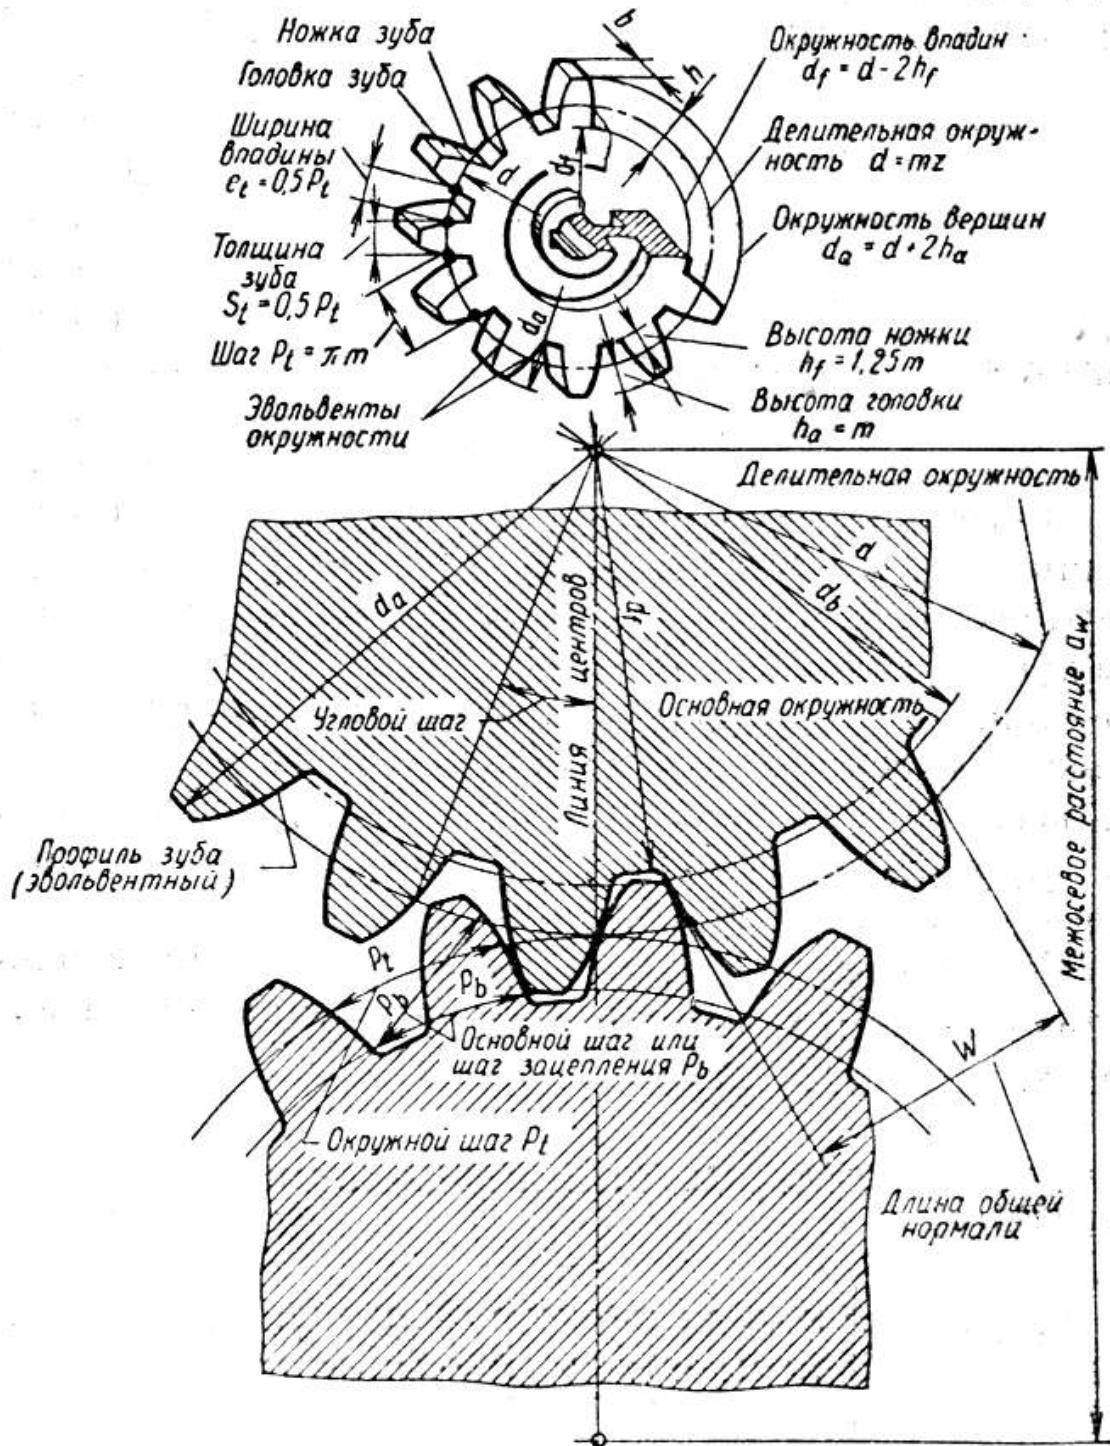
Зубчатые колеса в зацеплении. Параметры зубчатых колес, диаметр делительной окружности- d
